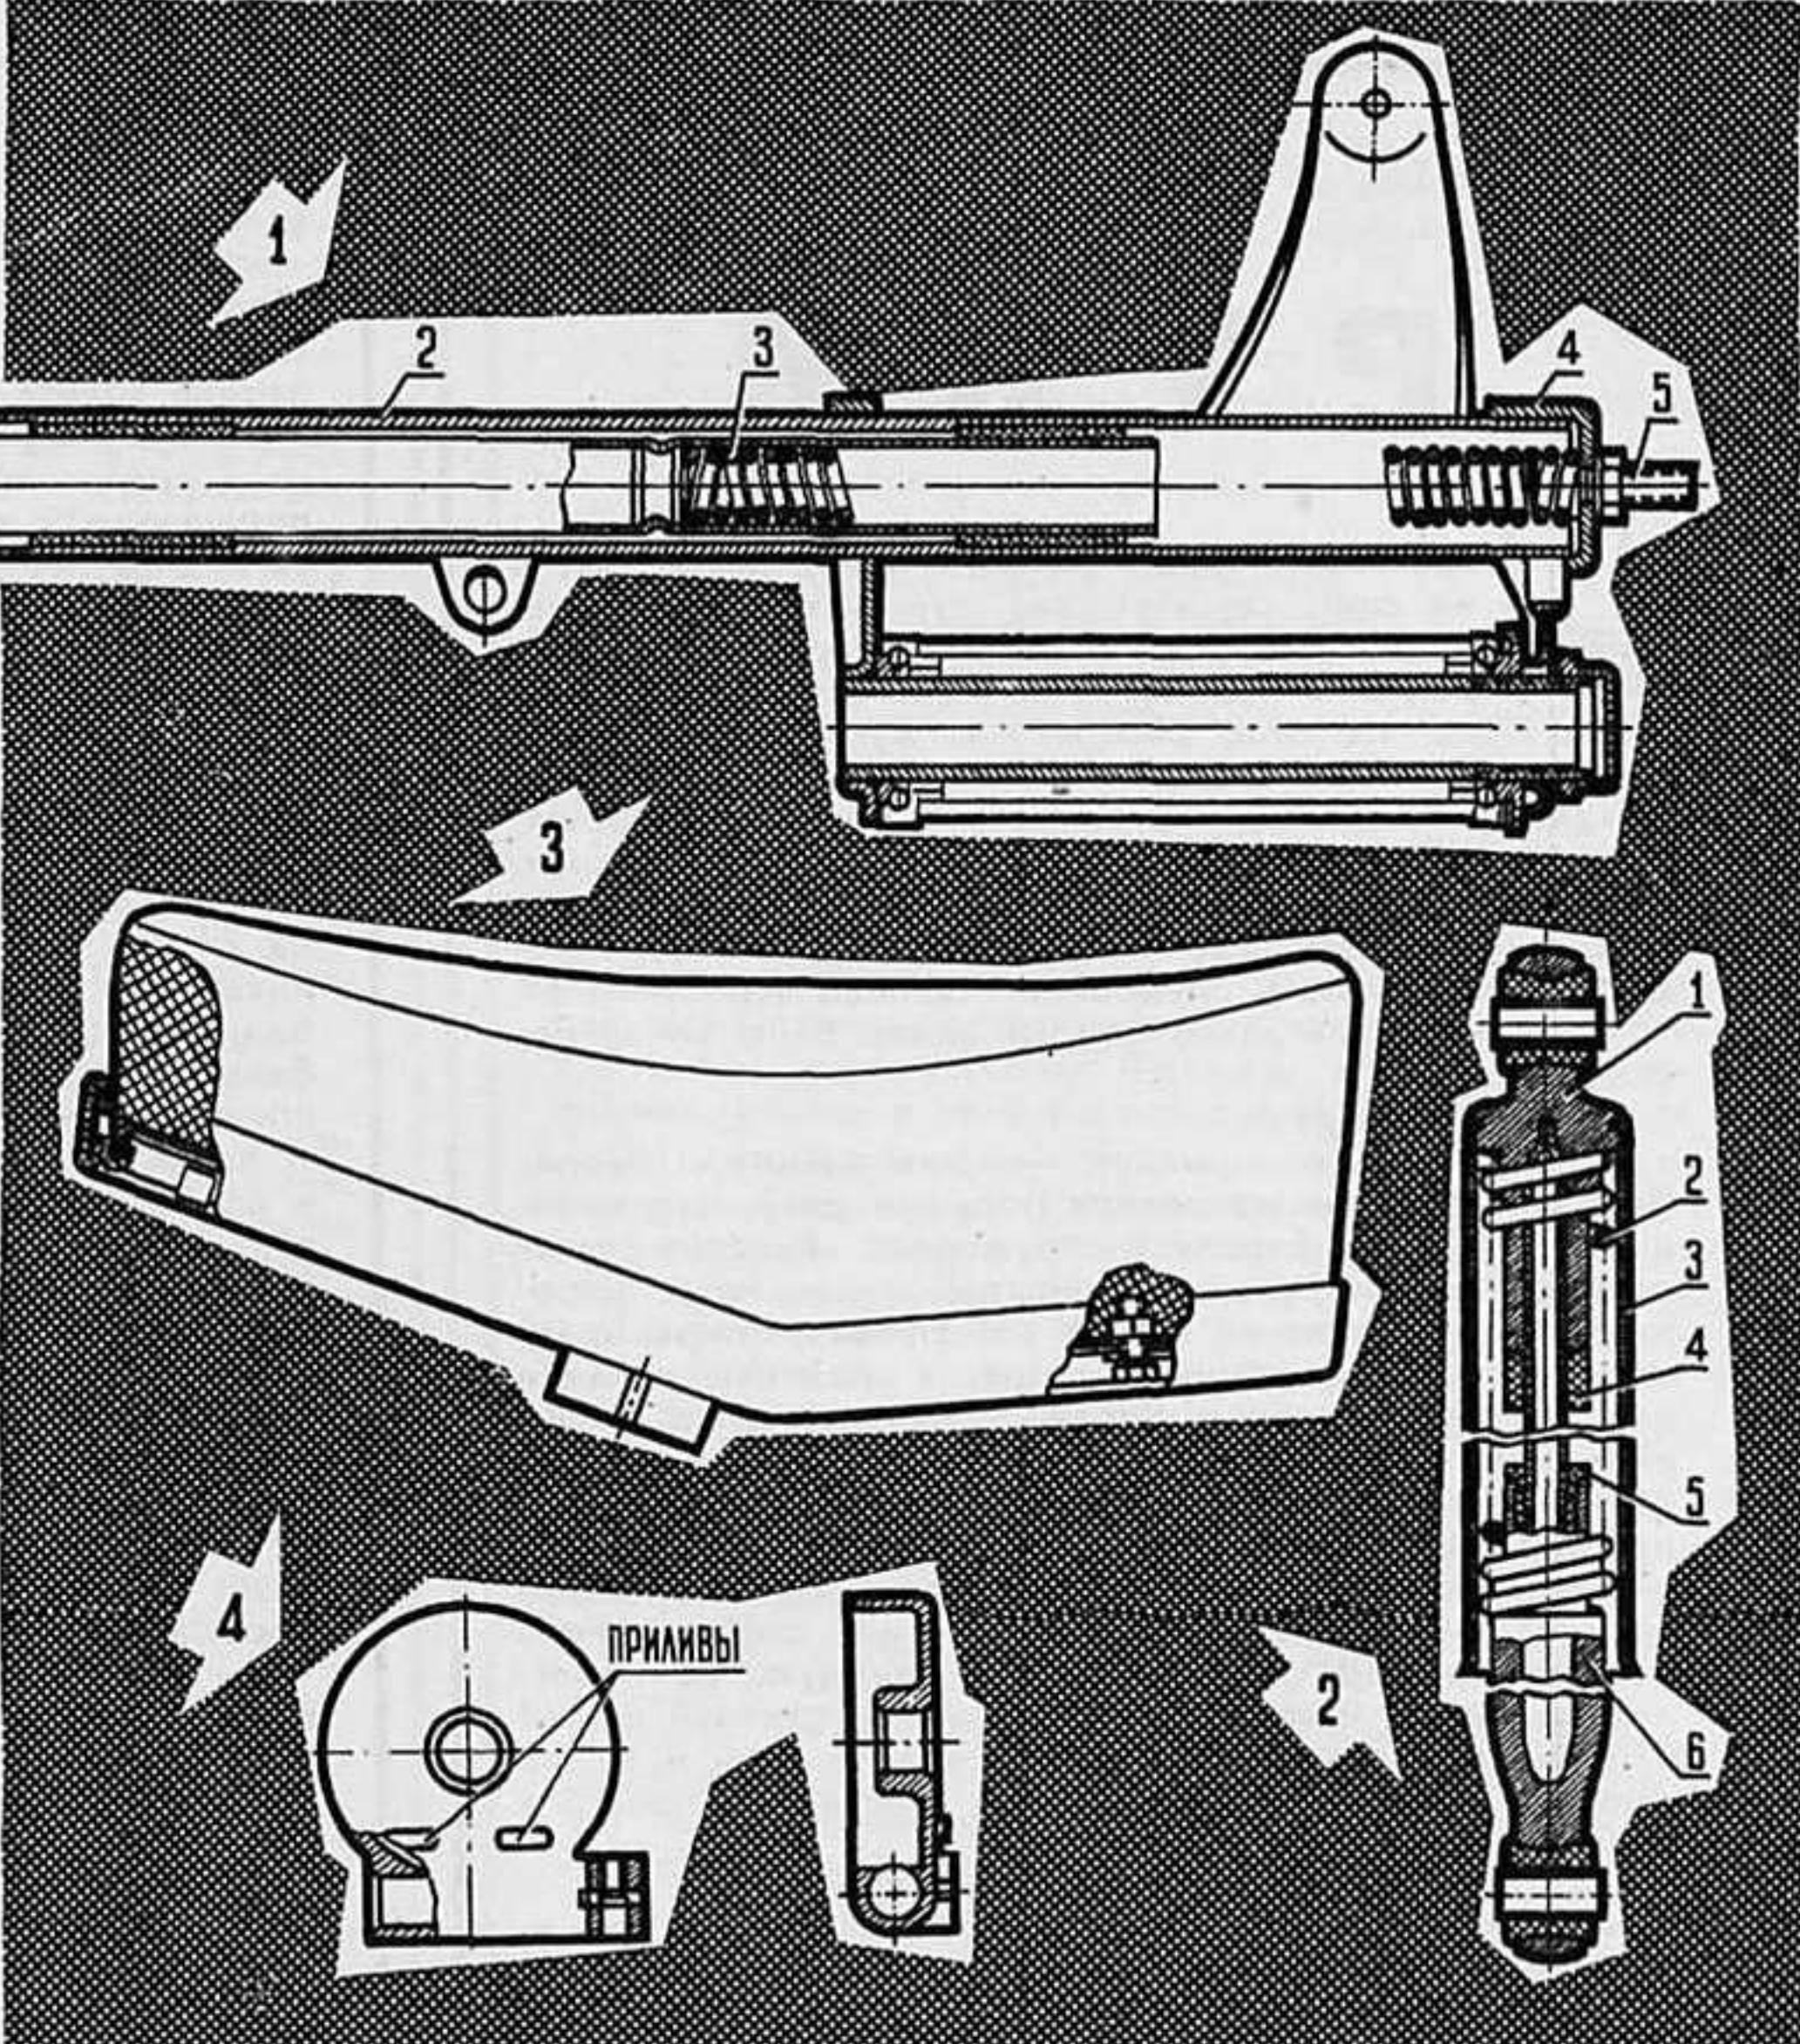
Новый амортизатор в сборе: 1 — головка в сборе; 2 — пружина; 3 — кожух; 4 — буфер; 5 — капроновая втулка; 6 — корпус в сборе.
